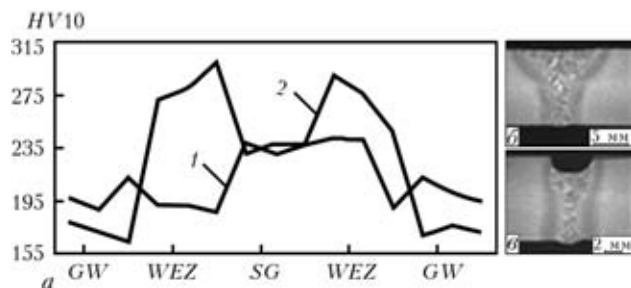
Зависимость твердости в области корня шва от пространственного положения сварочной головки (а) и макрошлифы, полученные с подкладкой (1, б) и без (2, в): GW, WEZ, SG — пространственное положение сварочной головки
